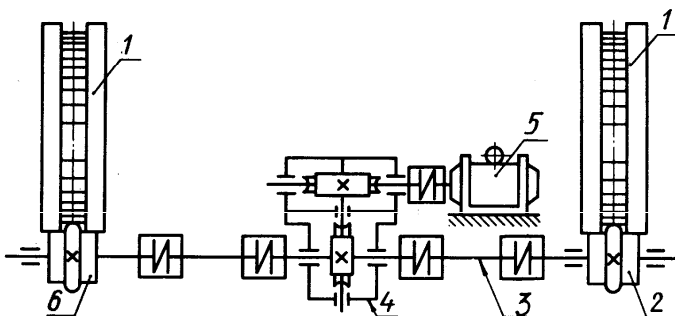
Кинематическая схема механизма вращения сборочно-сварочного стенда
